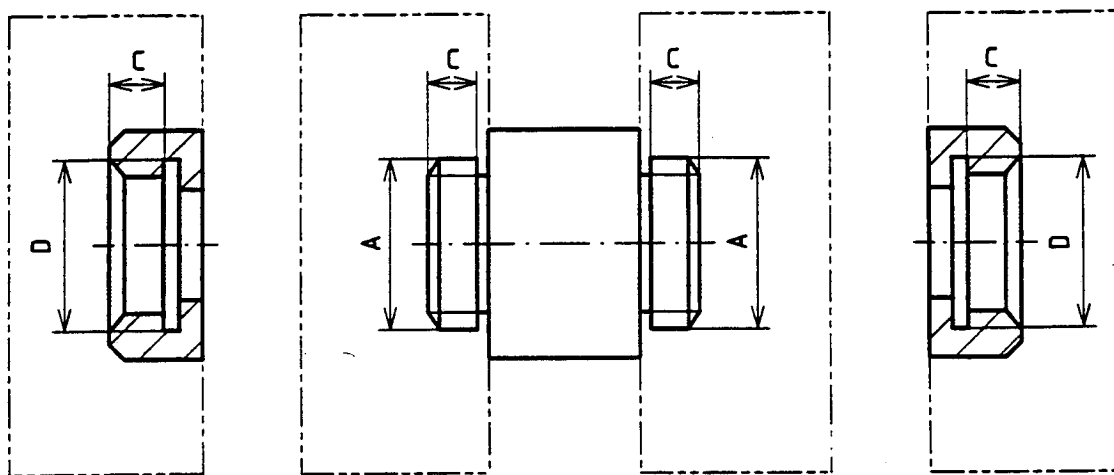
Durchgangsarmatur, Zu- und Auslauf
